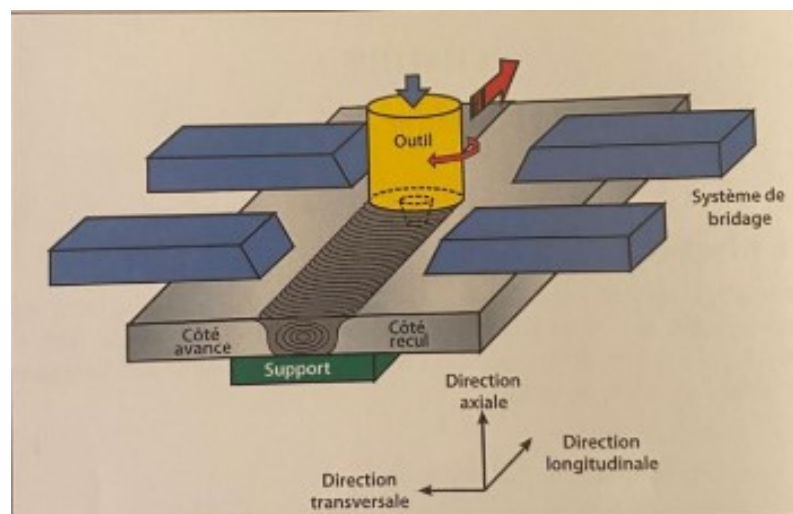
Composante principale de la cellule de soudage [6]
